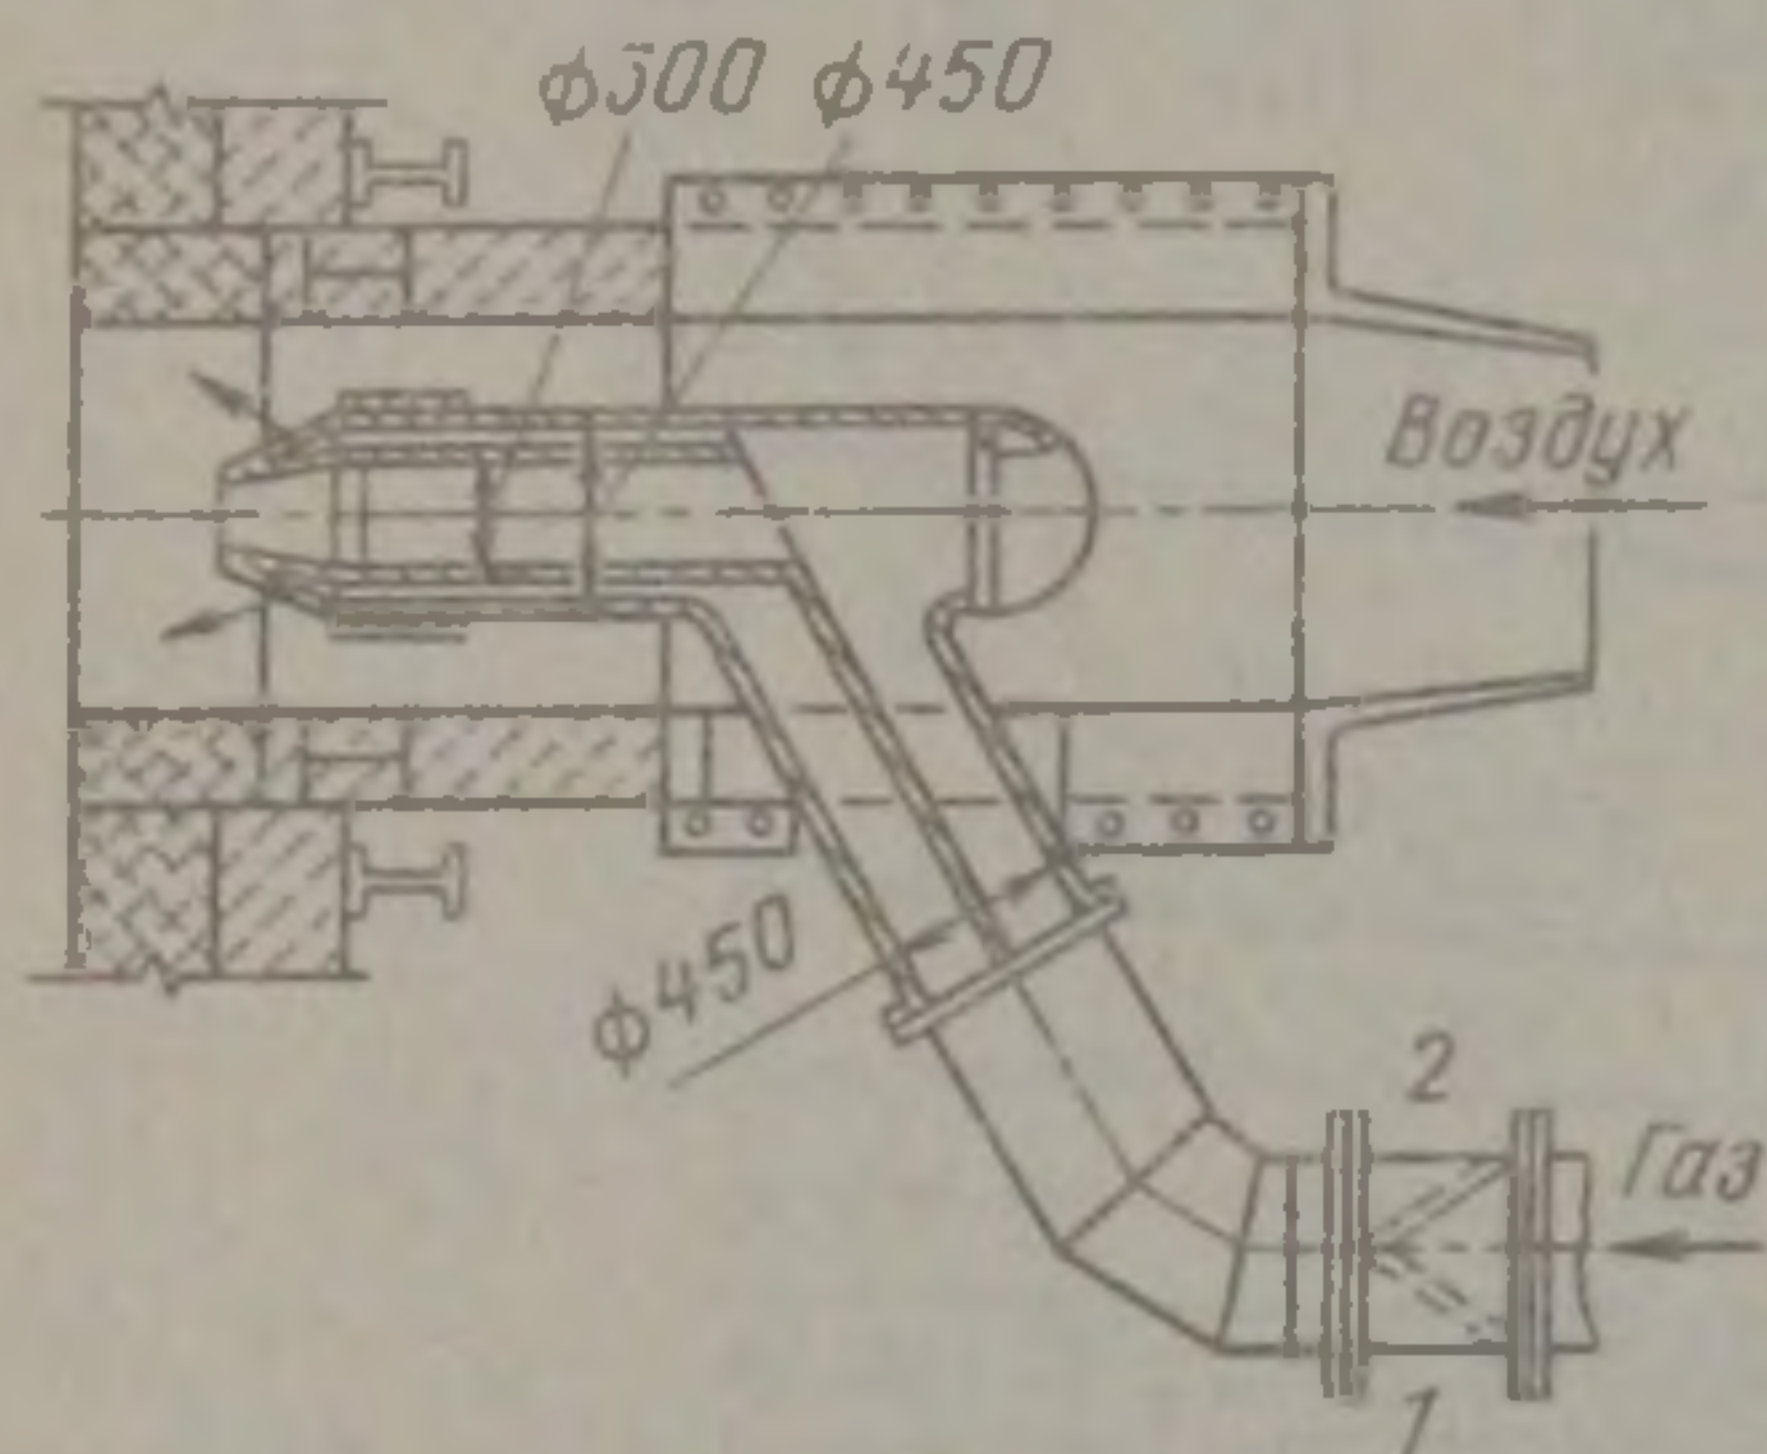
Горелка с регулируемой длиной пламени для нагревательных колодцев
